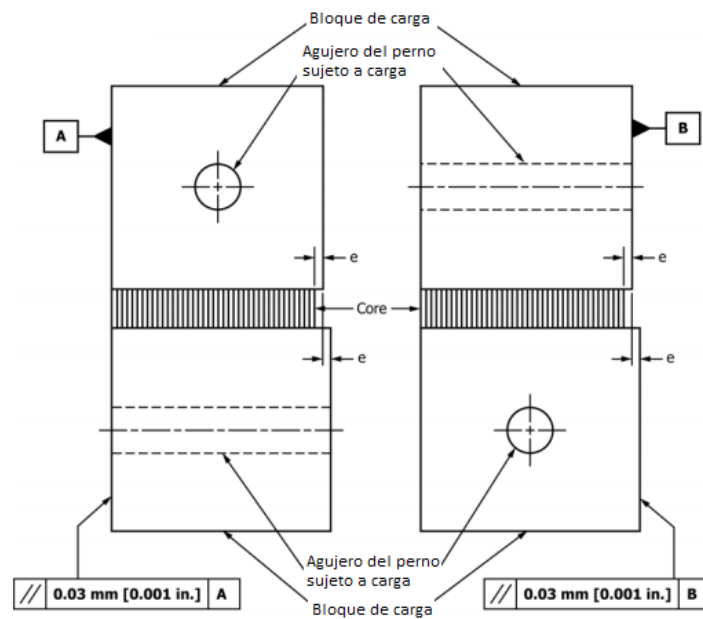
Dimensiones y tolerancias del conjunto adherido.
